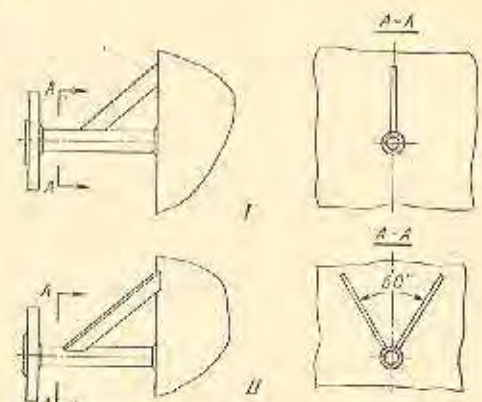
Конструкция присоединения малых штуцеров к стенкам сварных и паяных аппаратов
